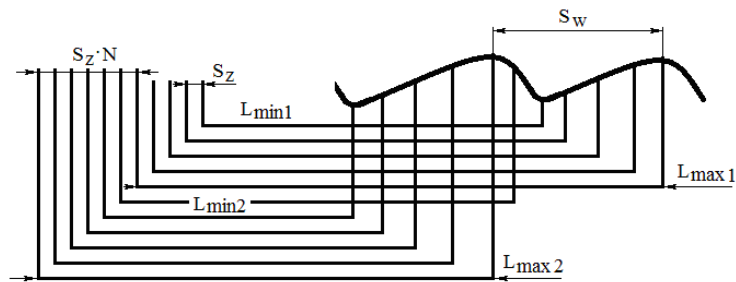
Схема визначення кроку хвилястості на обробленій поверхні після попутного фрезерування
